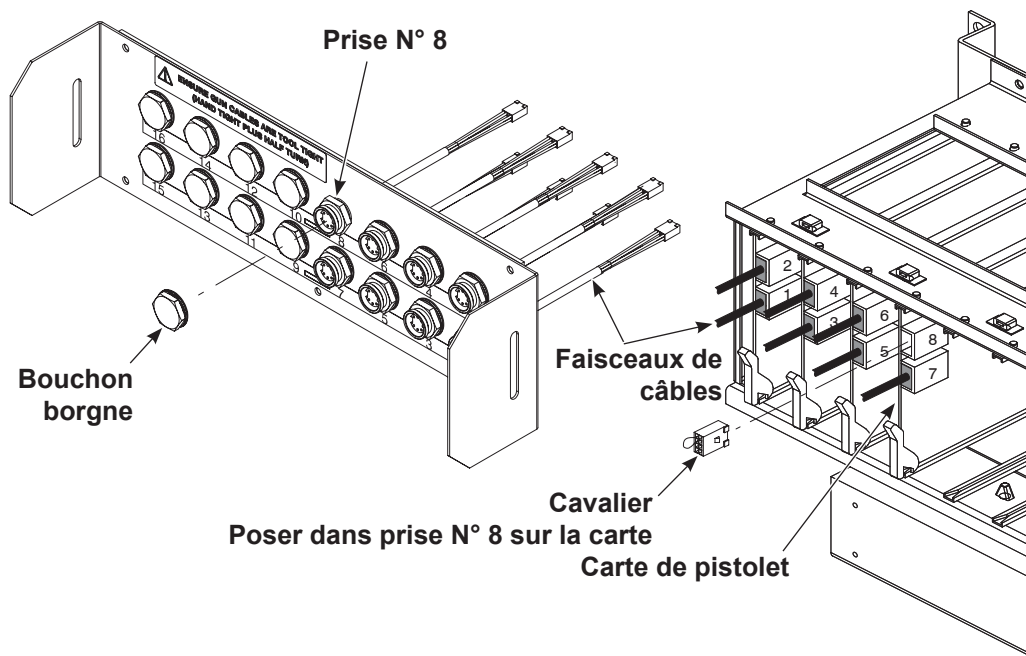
Pose du bouchon et du cavalier – Exemple illustrant un système à 8 pistolets utilisant 7 pistolets
